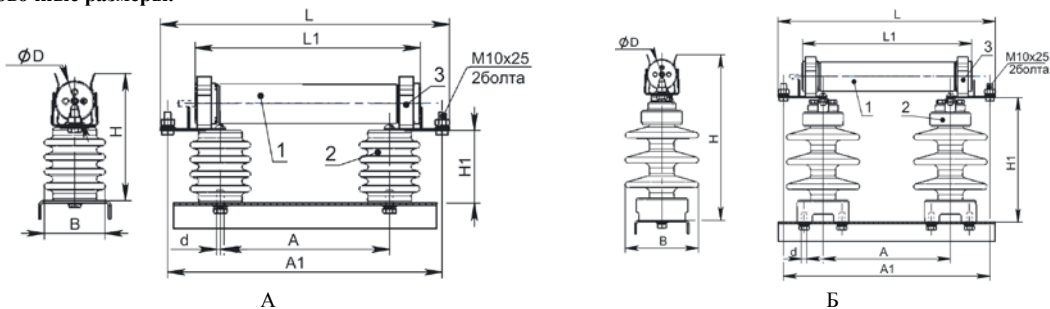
Габаритные и установочные размеры предохранителей ПКТ-101, ПКТ-102.
